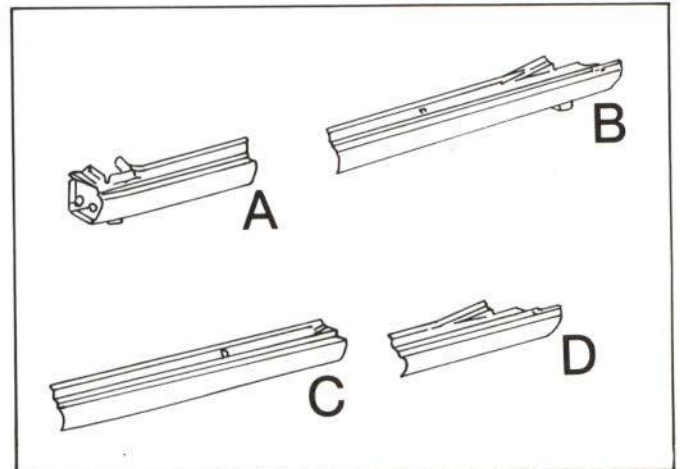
Secciones de ahorro del estribo bajo puertas.
